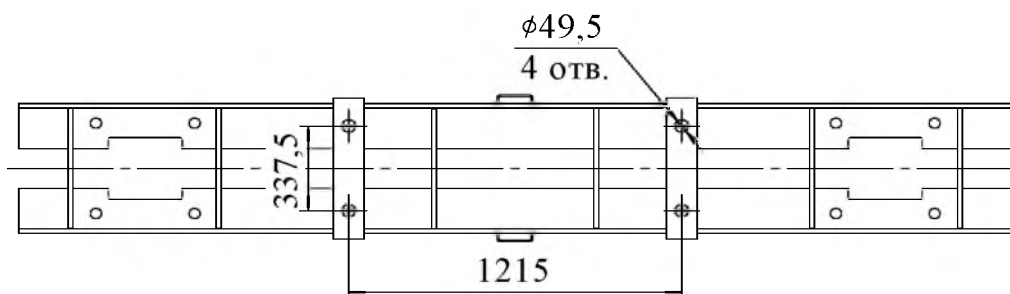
Разметка отверстий для крепления полюсов разъединителя РН□СК СЭЩ®-□-□-110/□ УХЛ1 к опорной конструкции (стойке)
